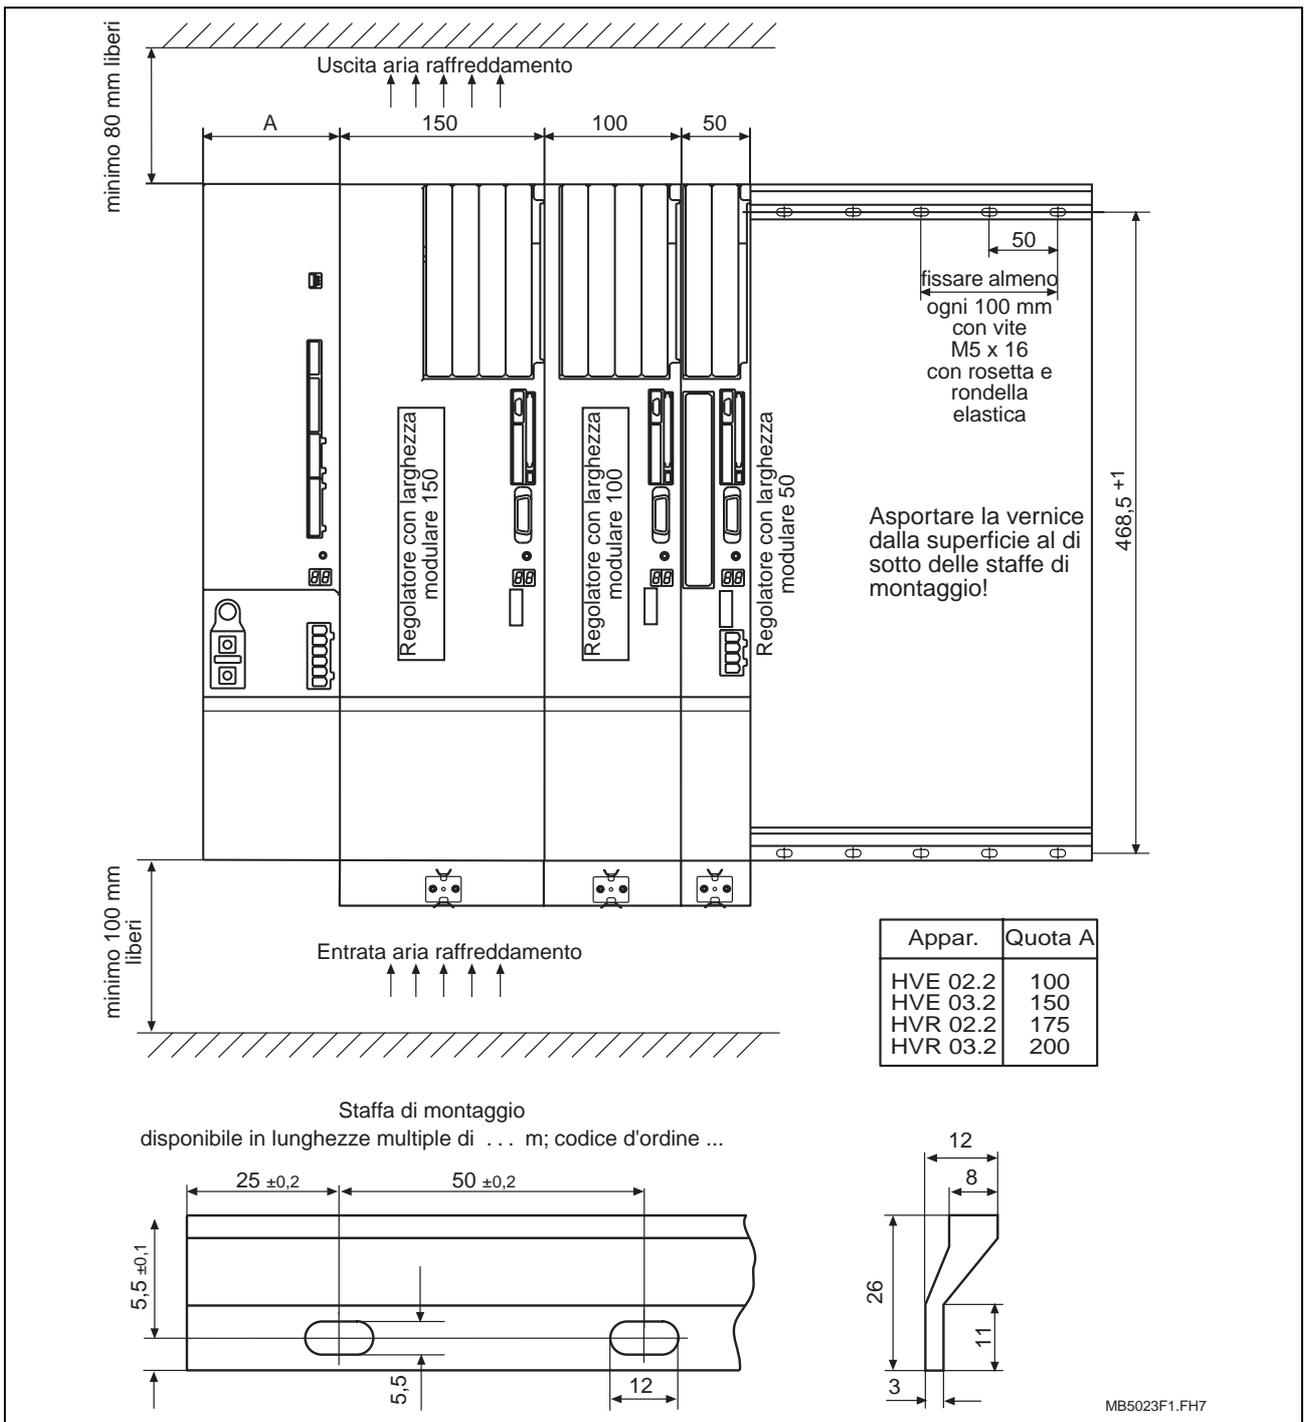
Montaggio degli apparecchi e fissaggio delle staffe
